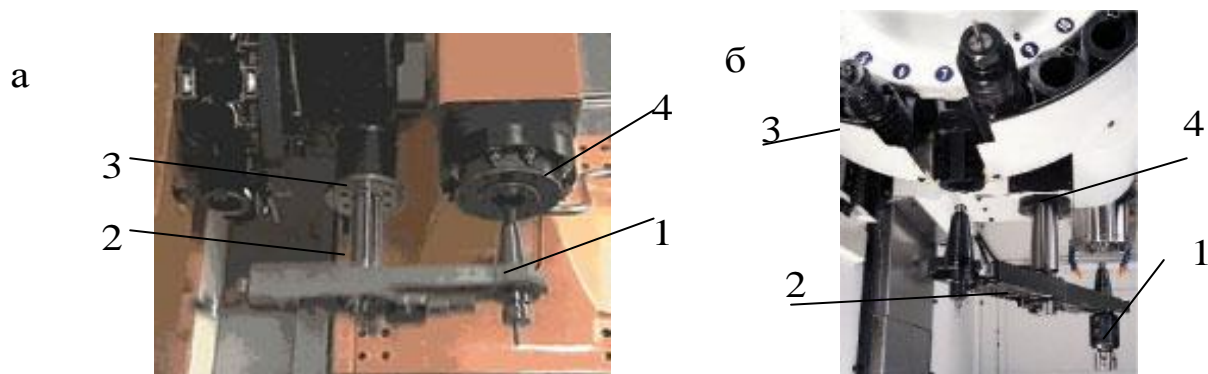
Конструктивная схема смены инструмента манипулятором: 1 – инструмент; 2 – манипулятор; 3 – магазин; 4 – шпиндель
